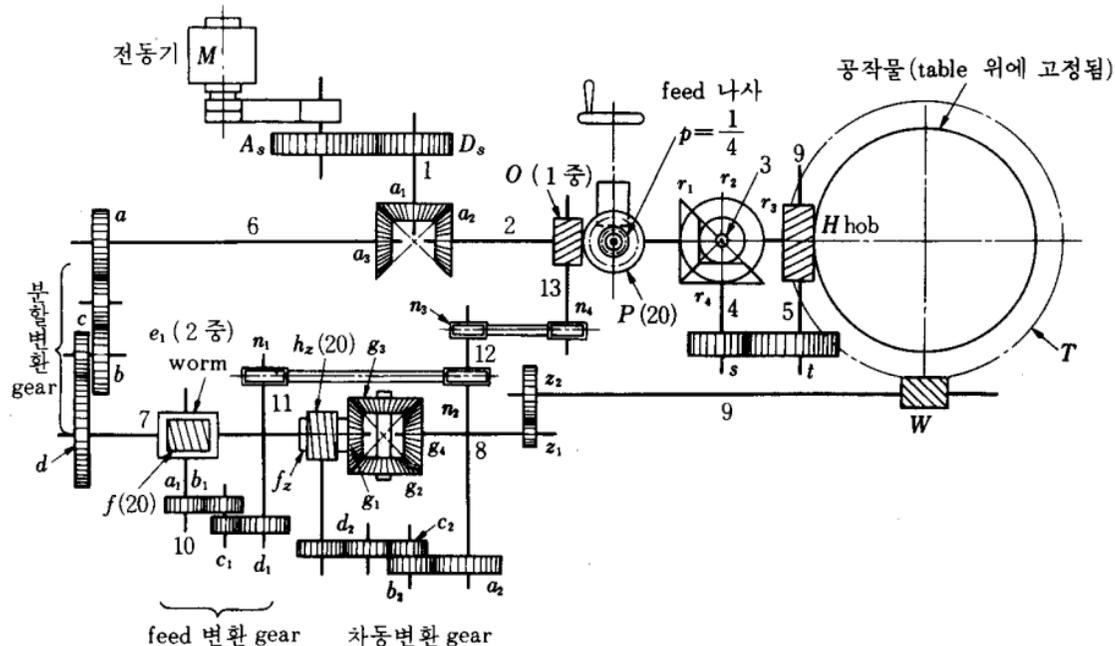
hobbing machine의 구동계통 (평면도)
